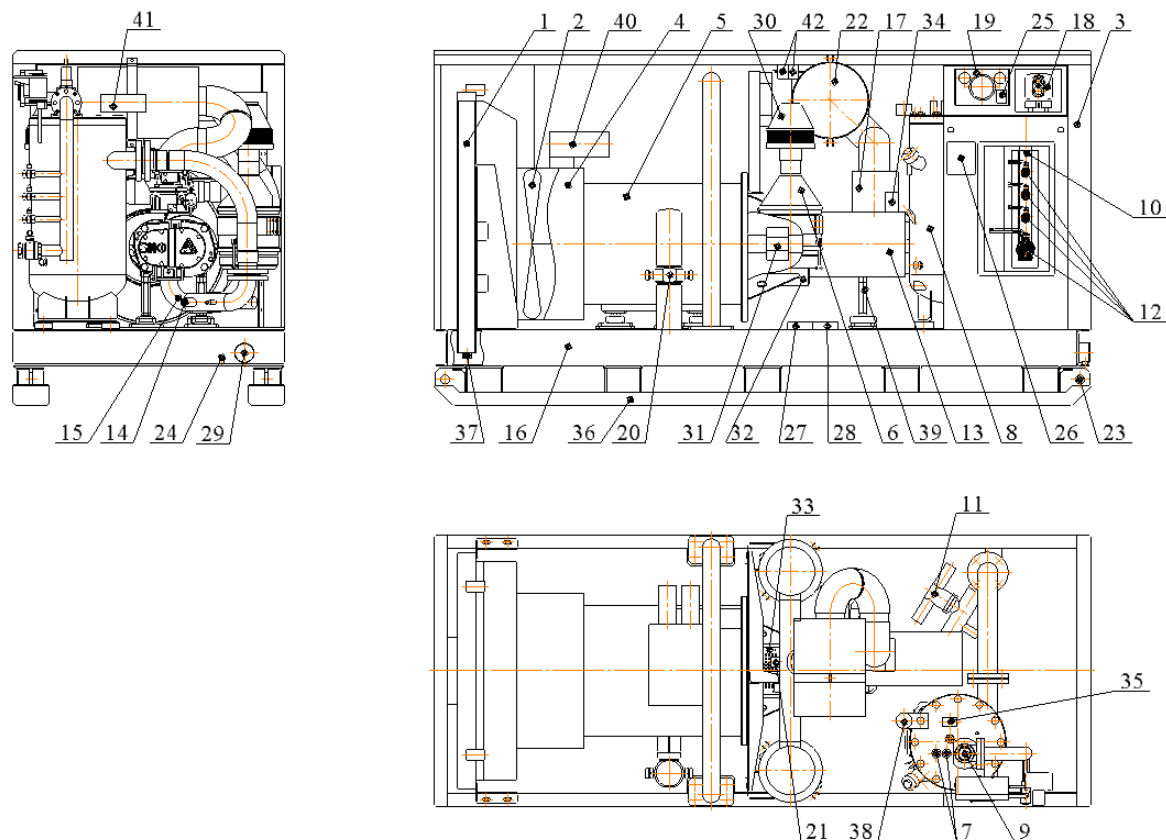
Габаритные и присоединительные размеры станций воздушно-компрессорных шахтных
